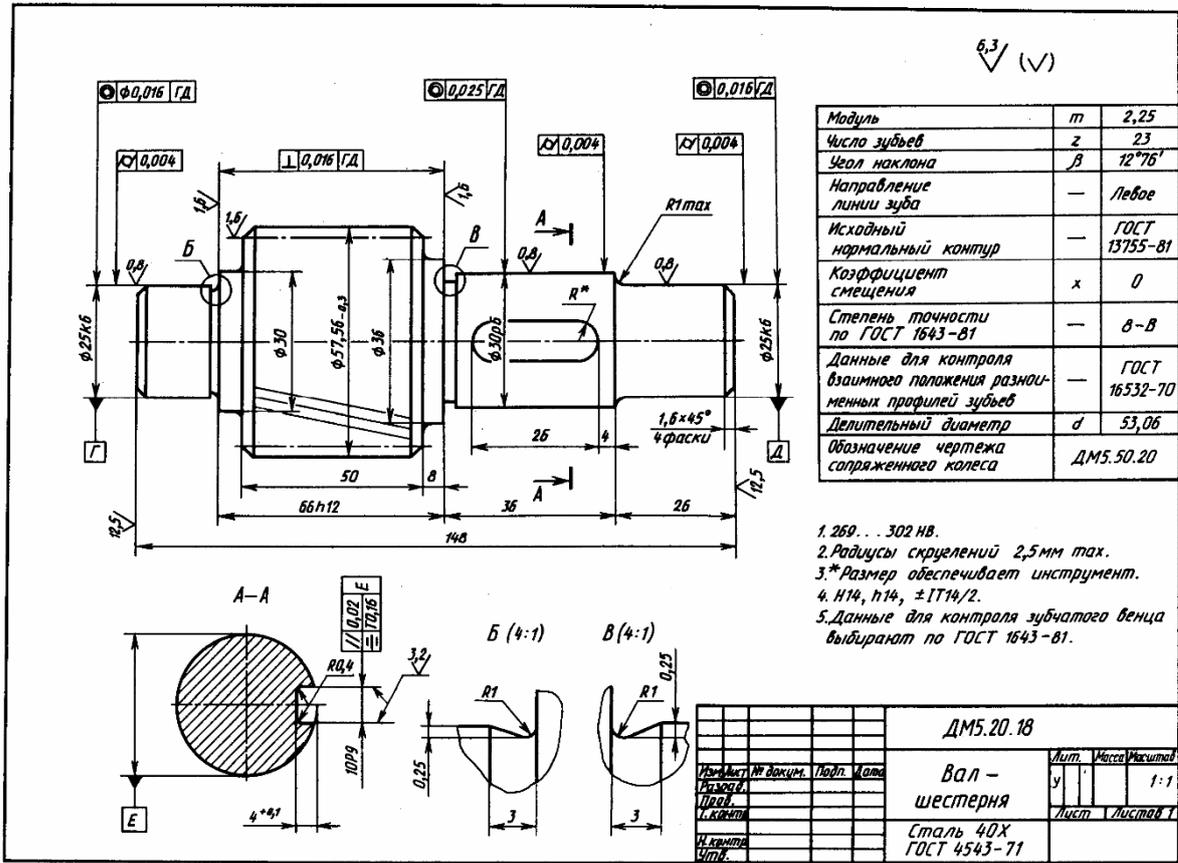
Чертеж детали «Вал-шестерня»
